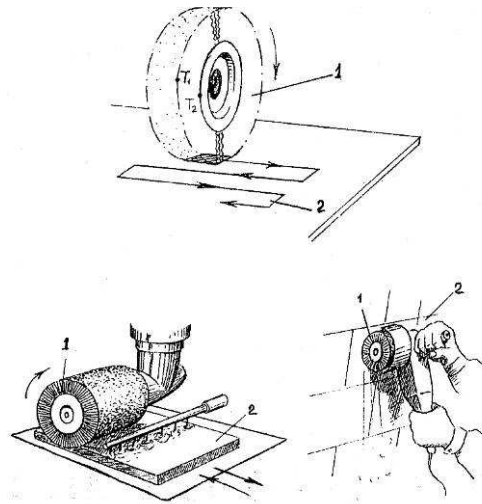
Обробка полімерно-абразивними інструментами:
